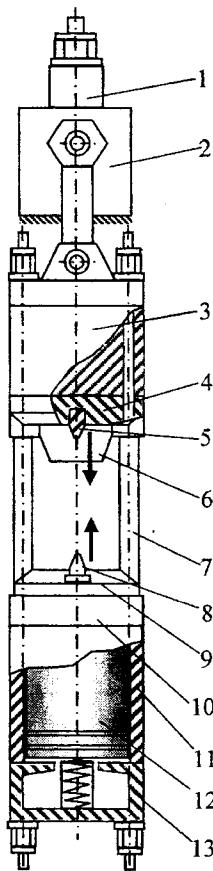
Схема устройства ножниц для импульсной резки заготовок:
